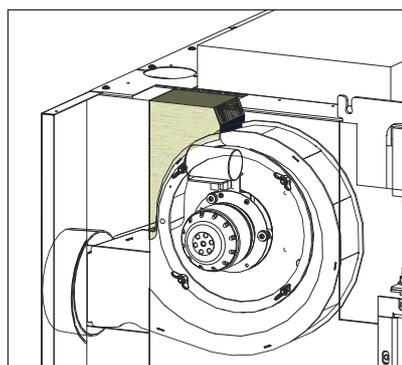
Inserimento dell'isolante nella parte superiore dell'attacco del tubo di scarico
